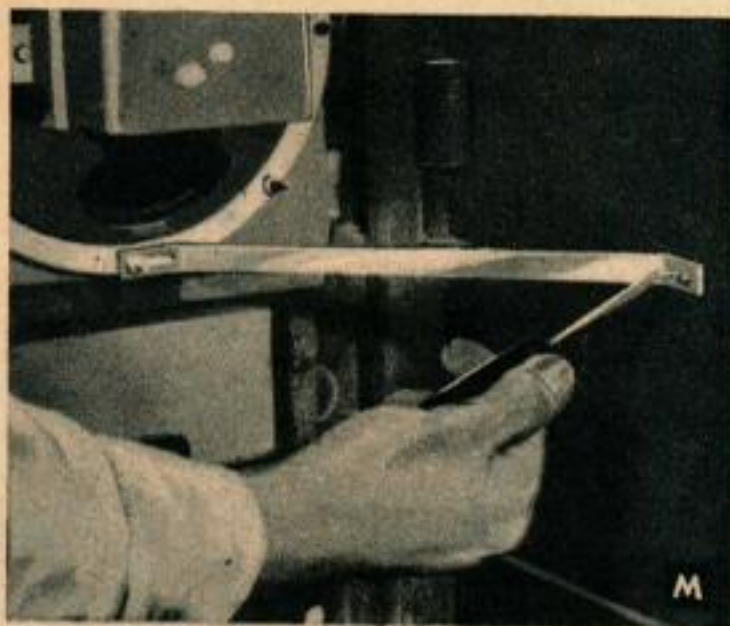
Photo M. — Dans certains cas de montage de haut-parleurs, l'ensemble, y compris le panneau de montage, vibre et fait du bruit d'une façon très désagréable, surtout si le contrôle est ouvert en plein. On a presque toujours de la place disponible, même sur les modèles à petit coffret, pour mettre une ferrure reliant le châssis du haut-parleur au côté du coffret, comme le montre la photo. Un bout de fer plat plié et percé suffit pour cela. Ce travail est facile à faire sur les postes montés sur table ou sur les récepteurs en ébénisterie. Dans un grand nombre de cas, le travail ainsi effectué est très utile car il donne lieu à une diminution appréciable des vibrations.
